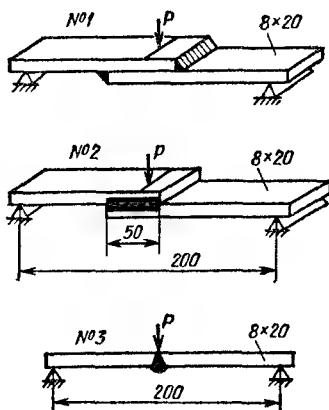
Схемы испытания сварных образцов на усталость
